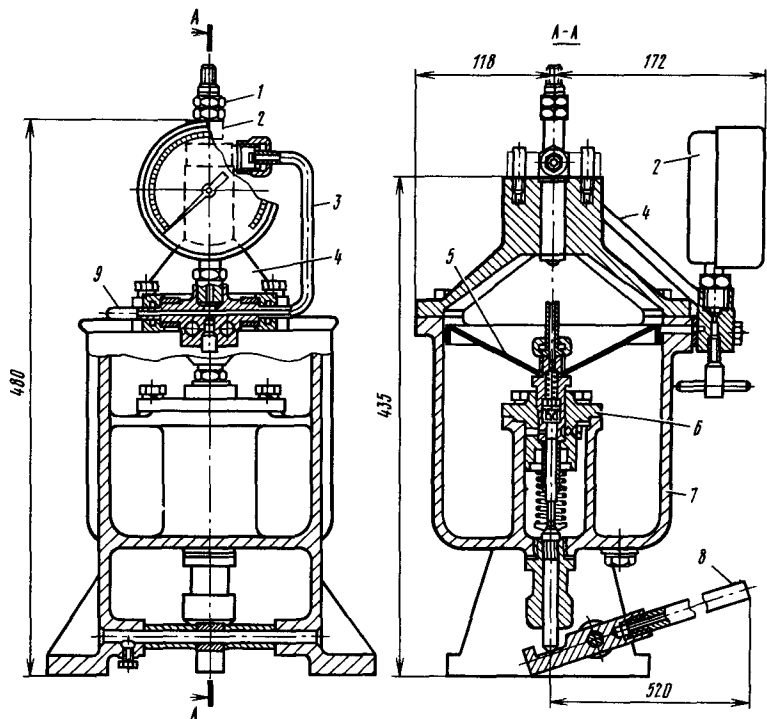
Универсальный стенд для проверки и регулировки форсунок:
